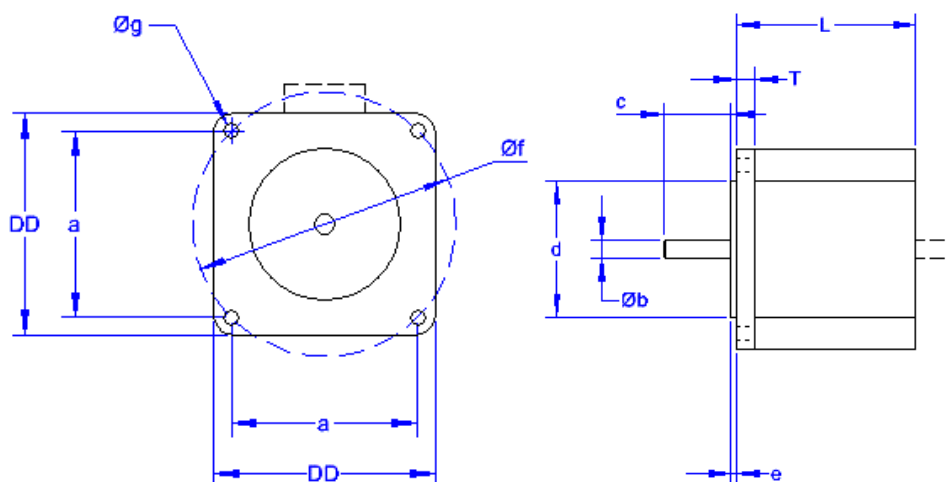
Desenho técnico das dimensões de um motor passo a passo segunda a norma NEMA.
